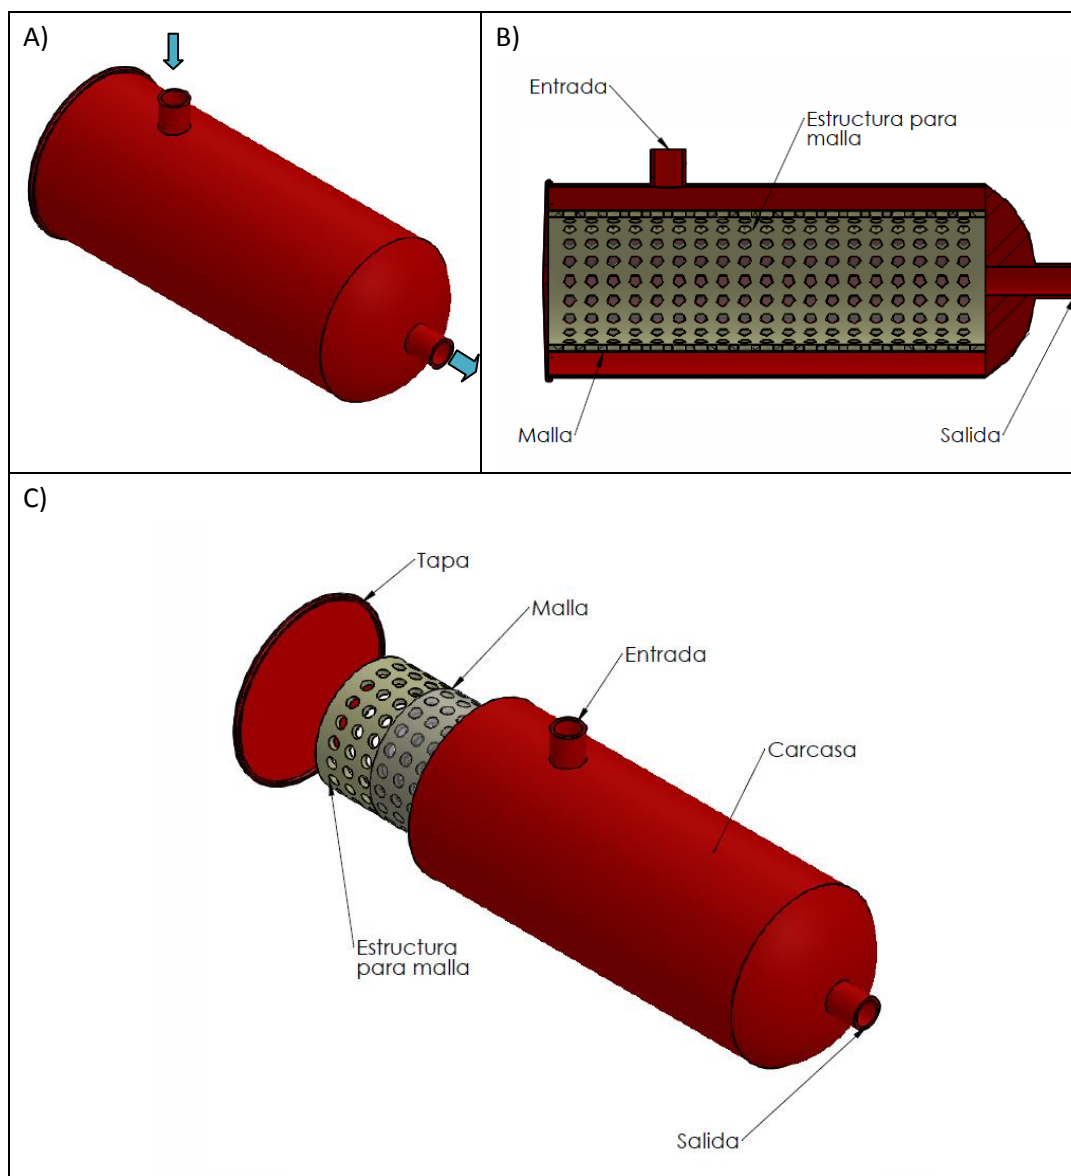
Esquema constructivo de un filtro de malla. A) Vista general exterior; B) Corte longitudinal; C) Vista explosionada. (Elaboración propia).
